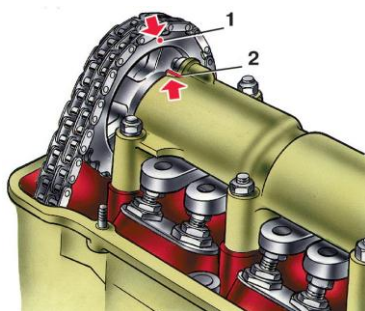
Установка поршня первого цилиндра в ВМТ на такте сжатия для регулировки клапанов: 1 – установочная метка на звездочке распределительного вала; 2 – установочный прилив на корпусе подшипников распределительного вала
